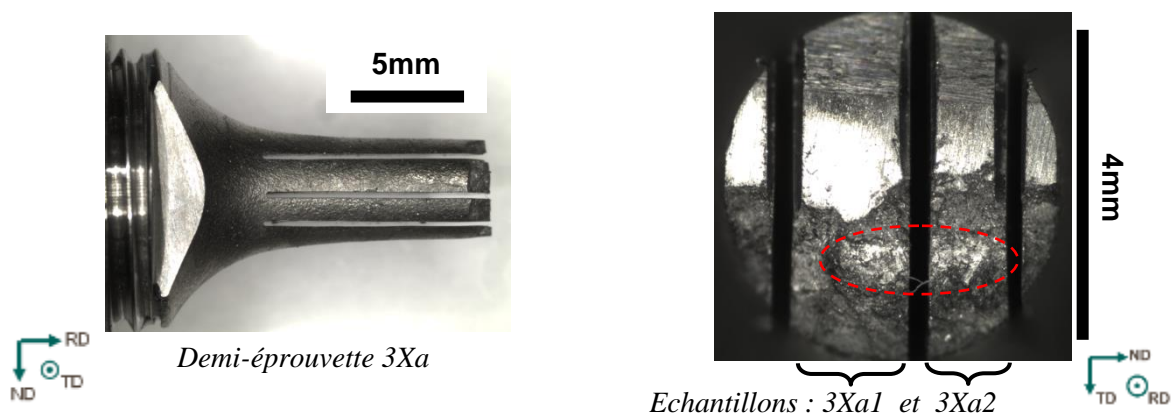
Demi-éprouvette 3Xa : Vue latérale et frontale après coupe longitudinale
